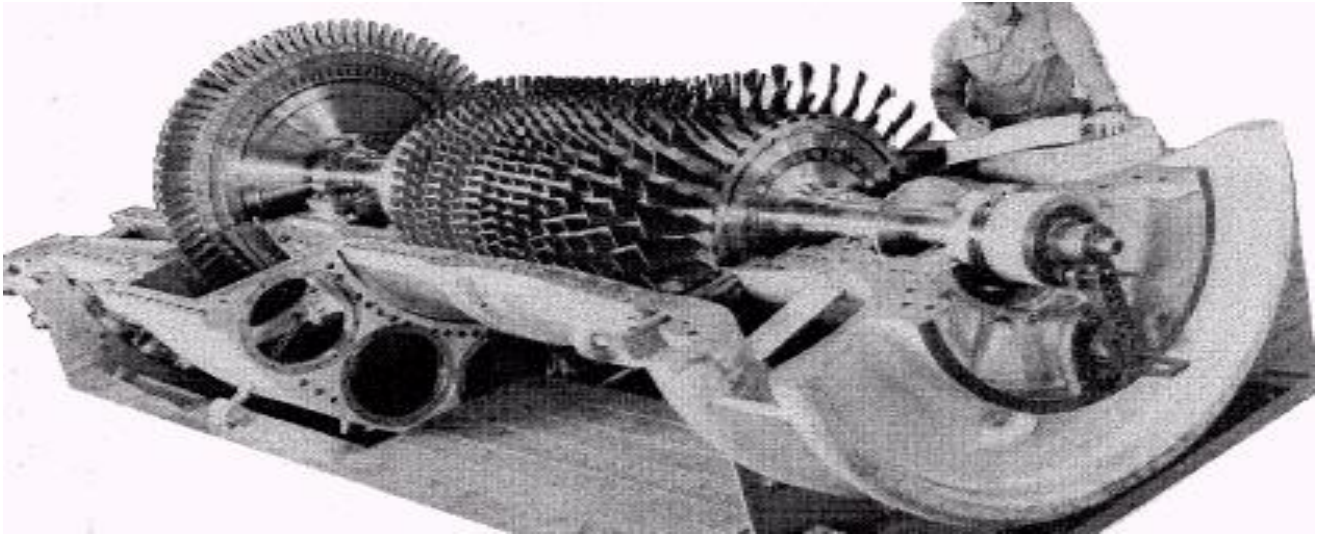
Ensemble corps compresseur et rotor turbine HP[5]
